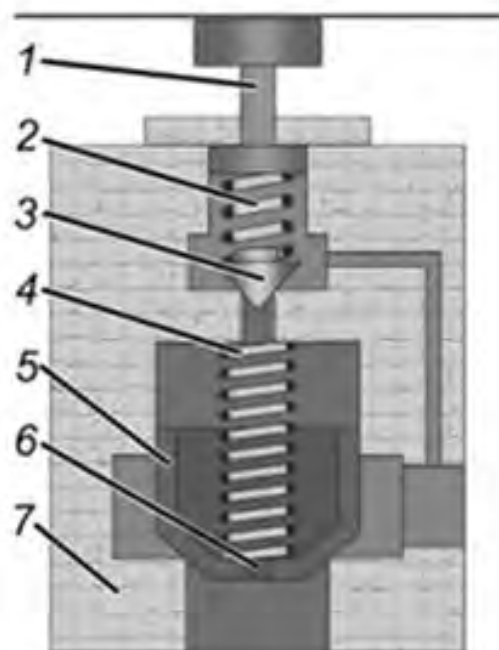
Непрямой предохранительный клапан: 1 - регулировочный винт, 2 - пружина, 3 - золотник, 4 - пружина, 5 - запорно-регулирующий элемент, постоянный дроссель, 7 - корпус
